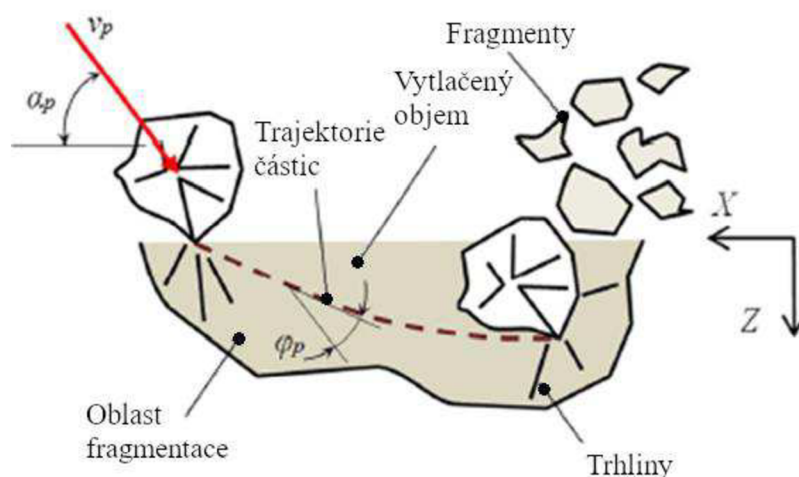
Zjednodušené schéma řezání čistým a abrazivním vodním paprskem [3].
